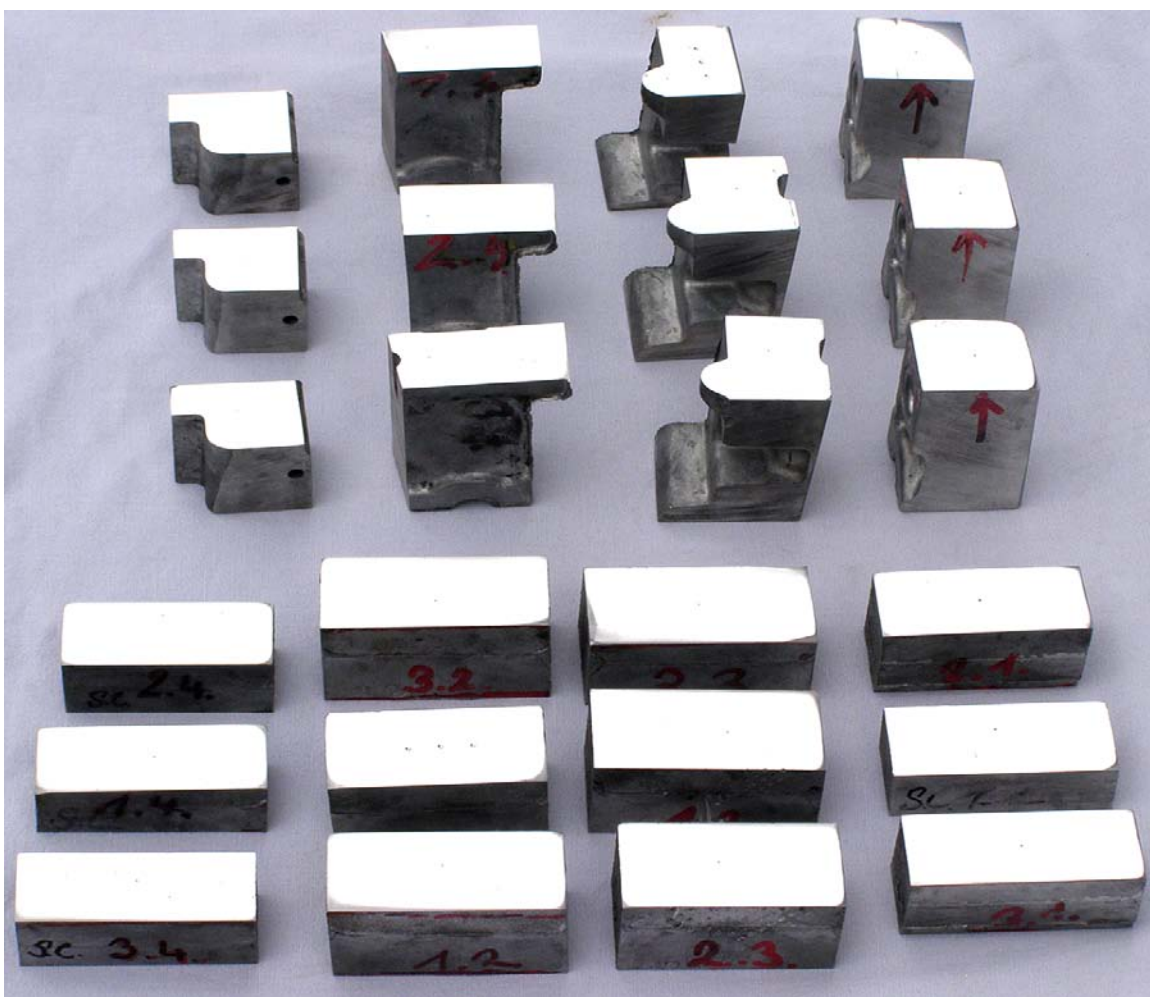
Postup odběru vzorků z místa B (spodní část) s použitím aplikace Squeeze – Casting a značení jednotlivých vzorků.
